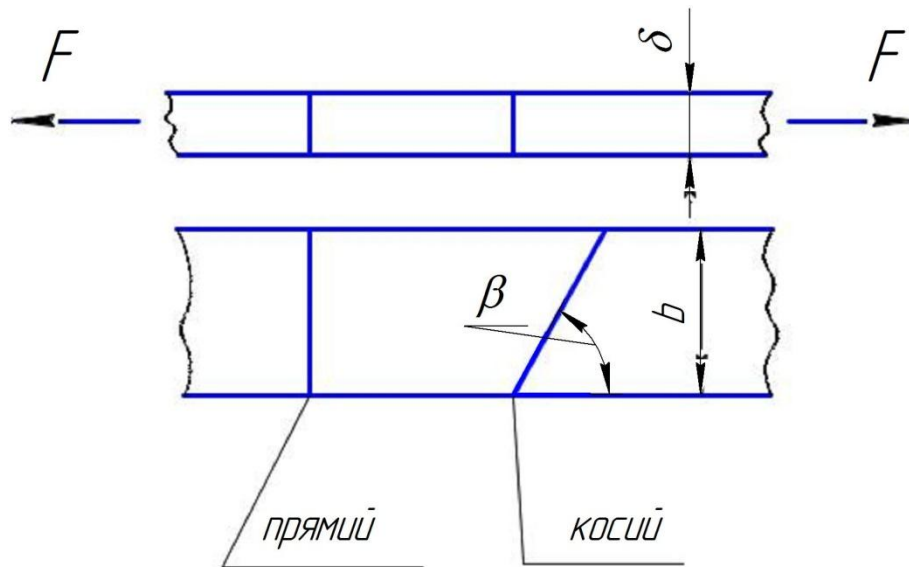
Розрахункова схема зварного з'єднання стиковим швом
